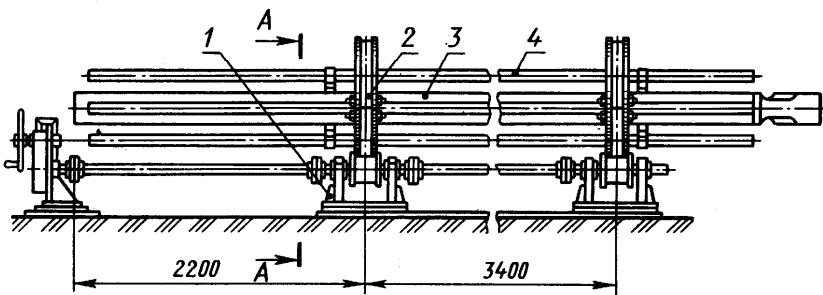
Установка для сварки балок рукоятей экскаватора
